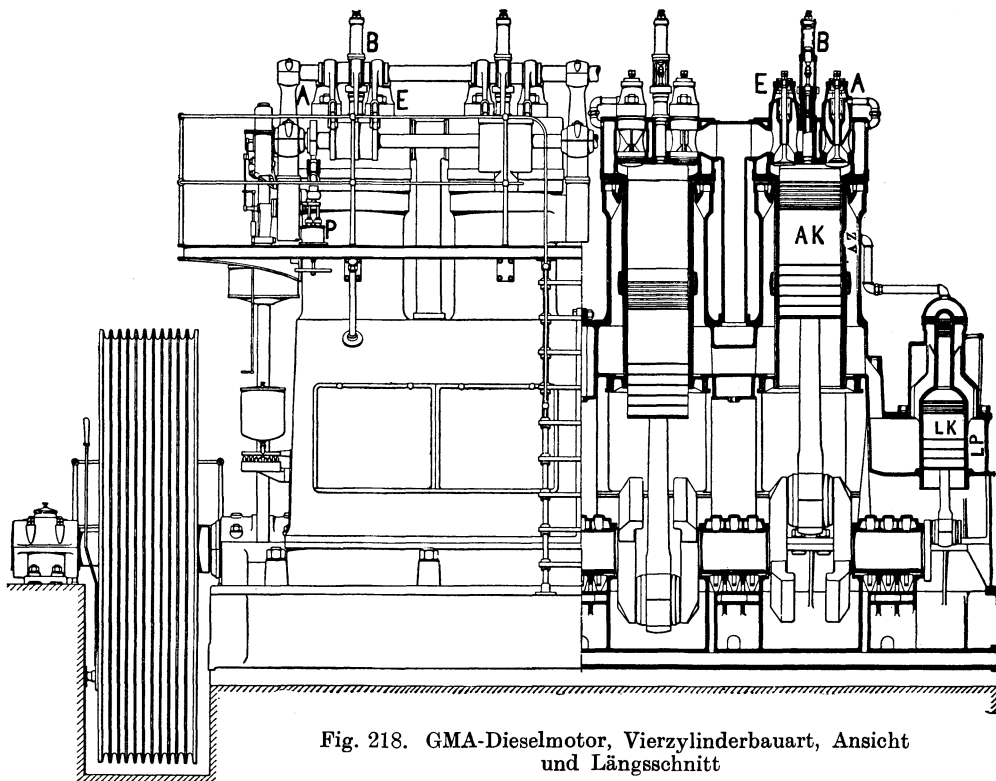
GMA-Dieselmotor, Vierzylinderbauart, Ansicht und Längsschnitt
